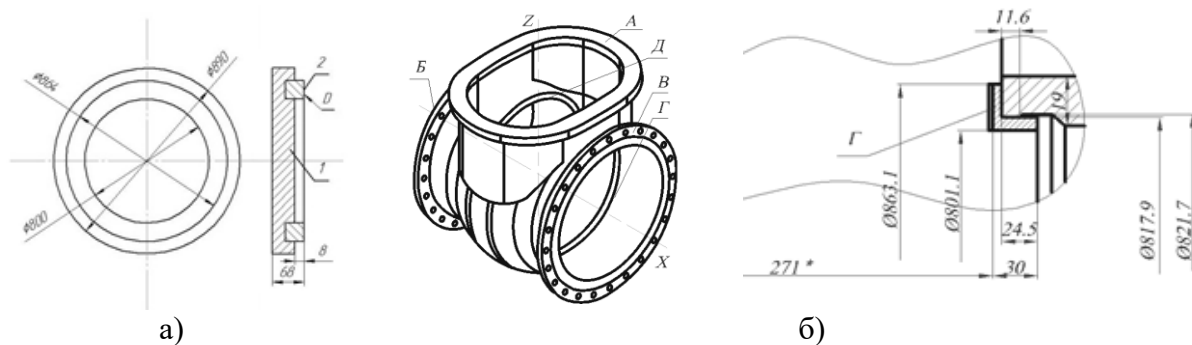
Ескізи деталей і ремонтваних поверхнь:
